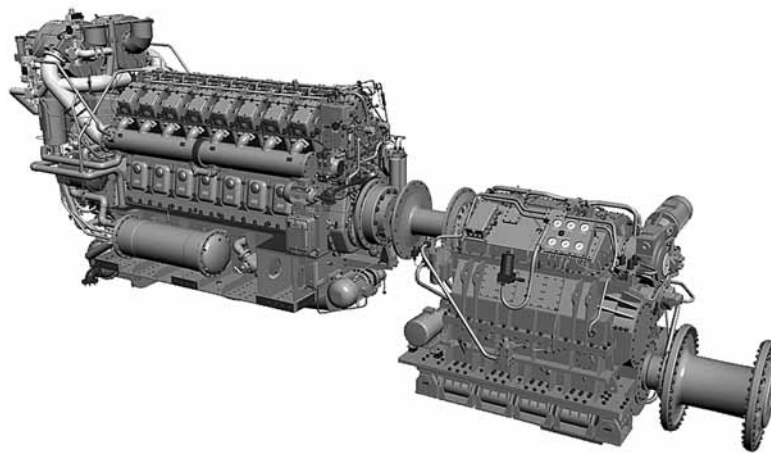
Дизель-реверс-редукторный агрегат ДРРА3700
